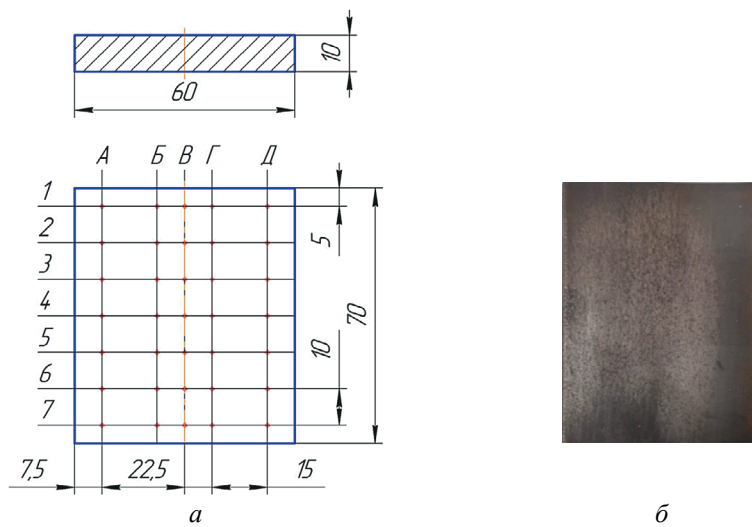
Схема измерений твердости (а) и опытный образец (б)
